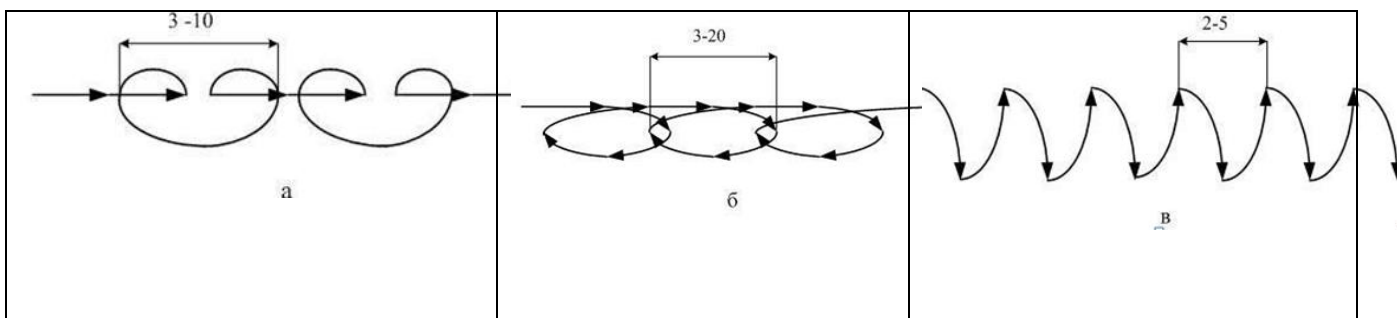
Схемы перемещения электрода при сварке плавящимся электродом в защитных газах для увеличения ширины шва: а и в – для получения равномерного провара по всей ширине шва, б – для получения плавного перехода от усиления шва к основному металлу на одну сторону от его продольной оси
